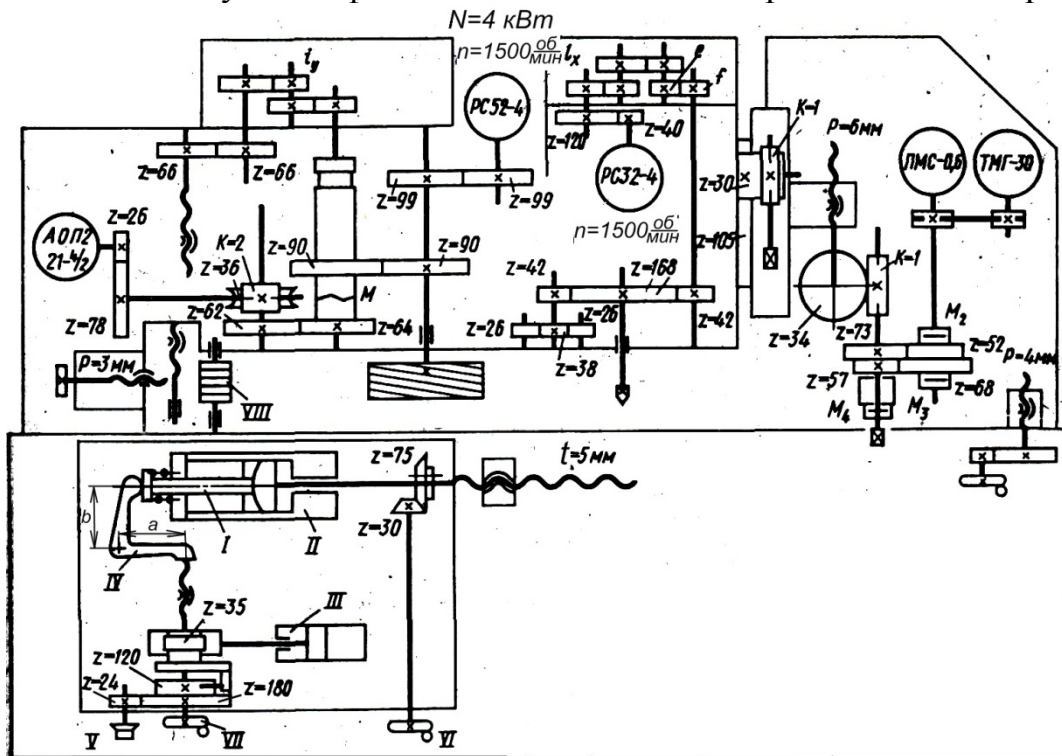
Кинематическая схема зубошлифовального станка модели 5В833
